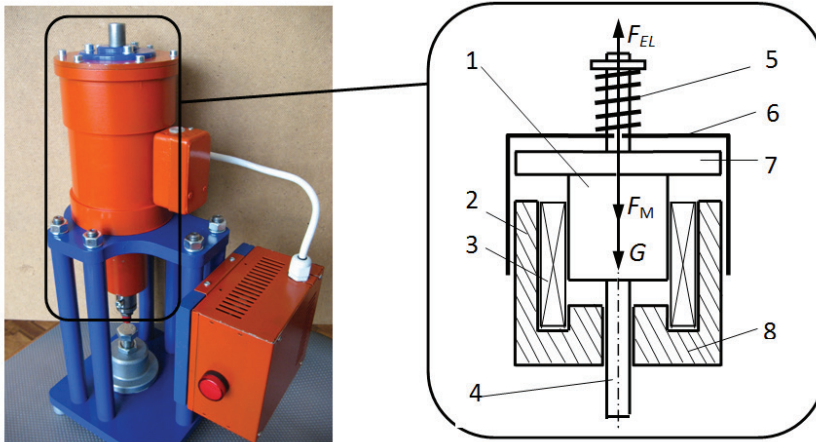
Внешний вид синхронного электромагнитного пресса и основные элементы синхронного линейного двигателя пресса: 1 – якорь; 2 – статор; 3 – обмотка; 4 – стержень для передачи энергии прессования; 5 – возвратная пружина; 6 – корпус, 7 – диск якоря, 8 – полюс, и основные силы, действующие на якорь: $F_M(t)$ – электромагнитная сила, $G(t)$ – сила тяжести, $F_{EL}(t)$ – сила упругости возвратного механизма (пружины).
